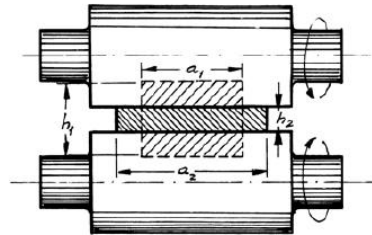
Rodillos Laminadores Vista Frontal.
